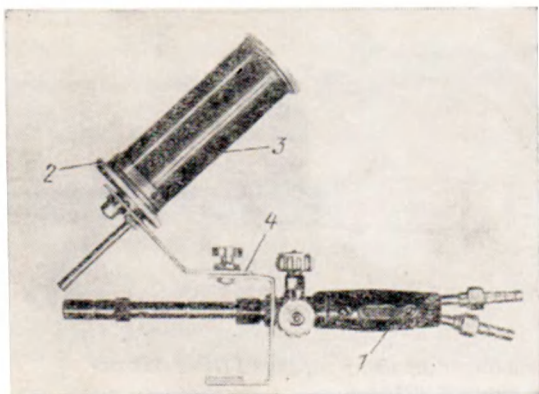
Горелка ГАЛ-6 для наплавки самофлюсующимися порошковыми сплавами
